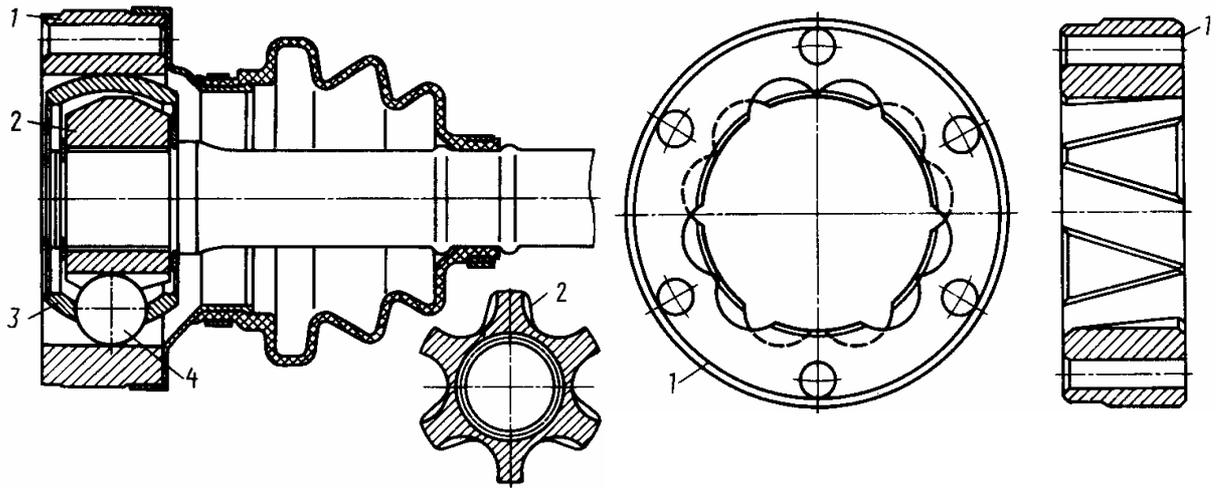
Шестишариковый универсальный карданный шарнир типа “Лебро”
